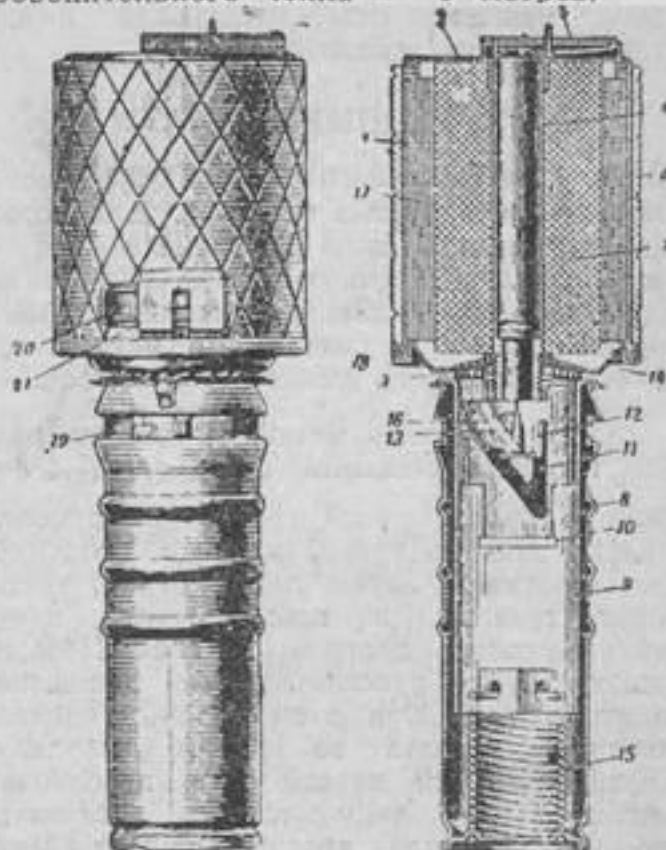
Граната образца 1933 года: 1—корпус; 2—крышка корпуса; 3—тормозящая звезда; 4—центральная трубка; 5—заводчик; 6—оборонительный чехол; 7—разрывной заряд; 8—наружная трубка рукоятки; 9—внутренняя трубка рукоятки; 10—вкладыш; 11—прорези; 12—боевая скоба; 13—ударник; 14—дно корпуса; 15—боевая пружина; 16—предохранитель завода; 17—лента; 18—опорные гайки; 19—заводчик предохранителя; 20—заводчик чехла; 21—штифт для закрепления чехла.
